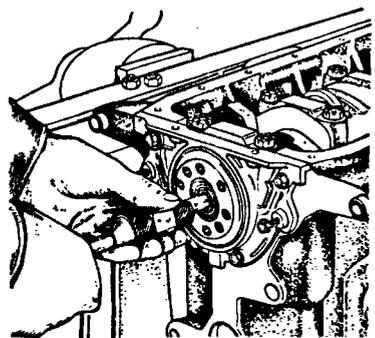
Выпрессовывание подшипника вала коробки передач из коленчатого вала выталкивателем А.40006
